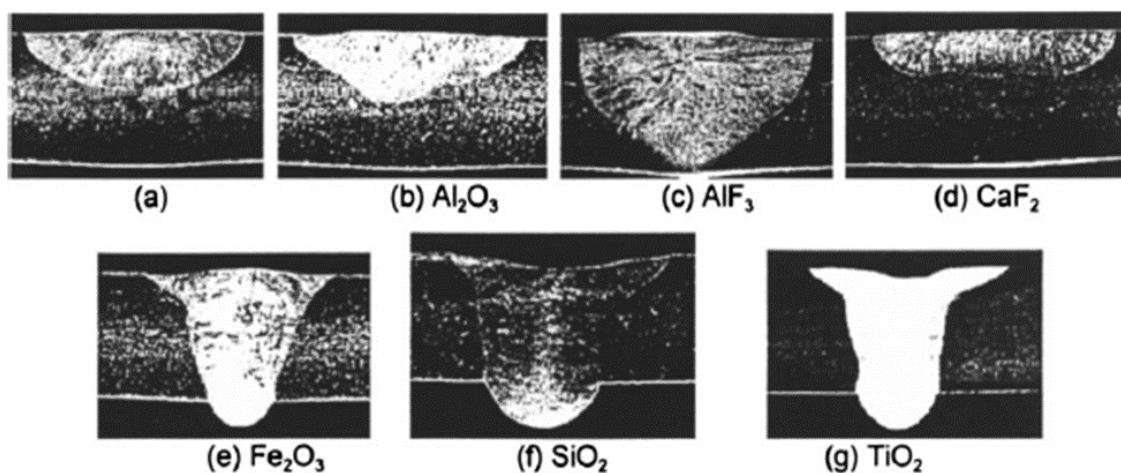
Seções transversais dos cordões de solda em placas de 5 mm do aço AISI 304 para: (a) TIG e (b a g) A-TIG.
